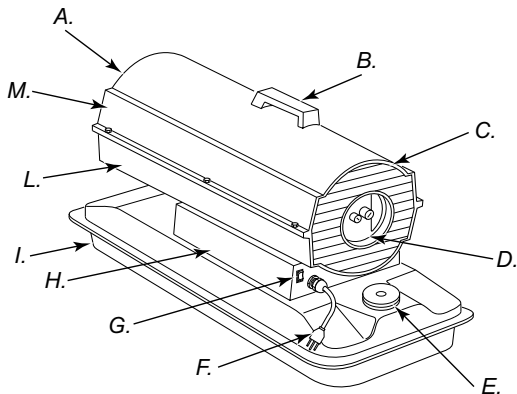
Model 35.000 e 70.000 Btu/Hr
